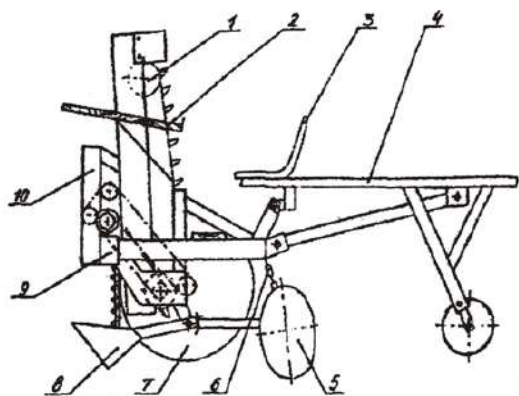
Принципиальная схема полуавтоматической картофелесажалки Л-202: 1 — высаживающий аппарат; 2 — платформа; 3 — сиденье; 4 — площадка для сидений и емкостей для картофеля; 5 — бороздозакрыватель; 6 — цепь бороздозакрывателя; 7 — опорно-приводное колесо; 8 — сошник; 9 — рама; 10 — сцепка
